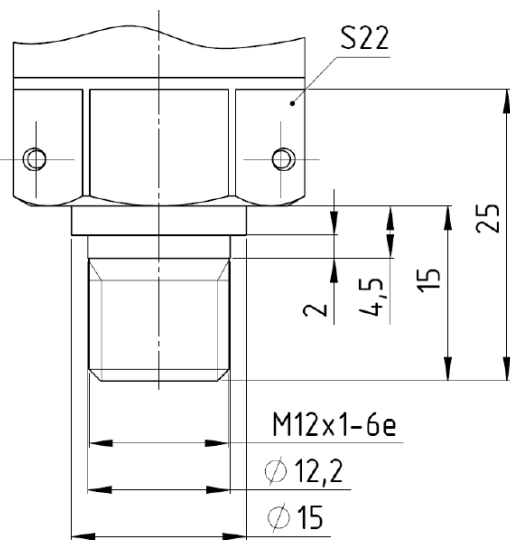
Присоединительный штуцер тип 3 по ГОСТ 19125-90, исп. 1, черт. 4
